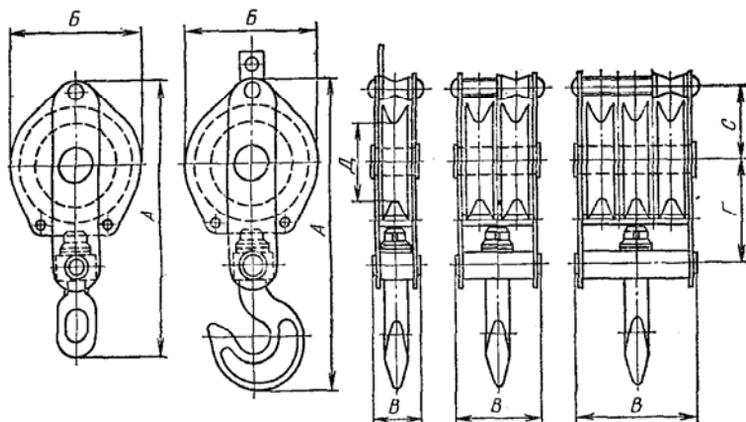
Блоки конструкции Каширского завода металлоконструкций
